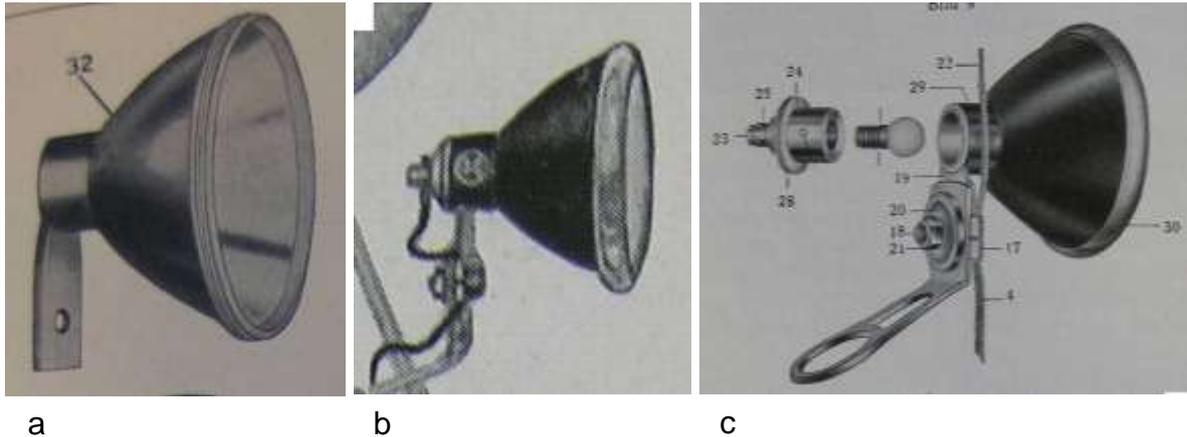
Lichtanlage mit zweiadrigem Kabel: a) Lampengehäuse, b) Lampe und Masseklemme gemeinsam mit dem Lampenhalter verschraubt, c) Auswechseln der Glühbirne
